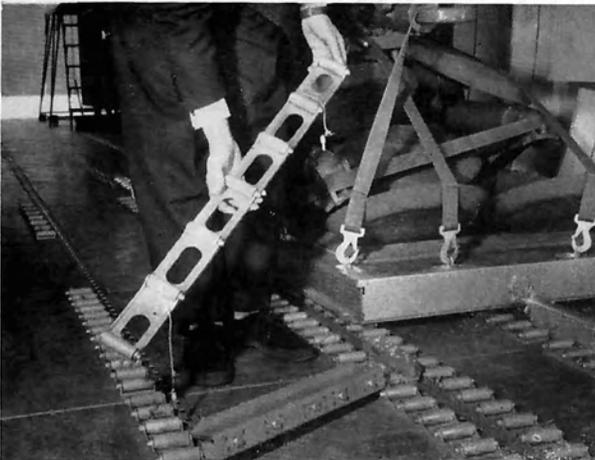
Rollschienen nach Art kleiner, aber sehr tragfähiger Rollenbahnen gebaut. Für die Montage in Fahrzeugen und Flugzeugen
